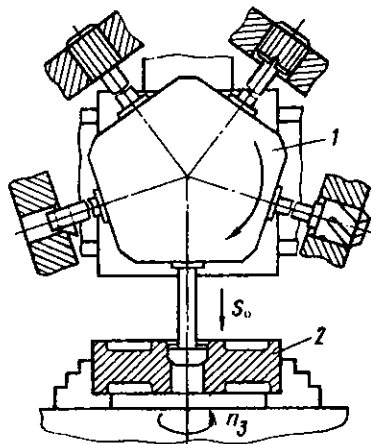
Схема обработки заготовки на токарно-карусельном станке с использованием револьверной головки: 1 – револьверная головка; 2 – заготовка
